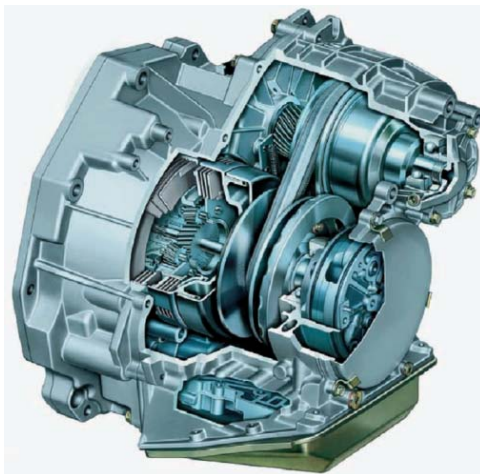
Загальний вигляд коробки передач з клиноремінним варіатором
